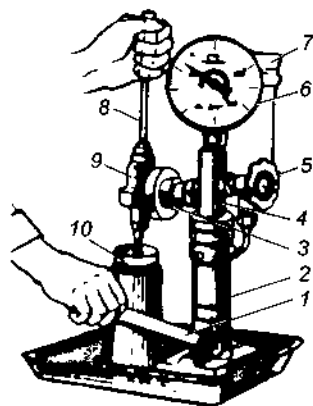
Проверка и регулировка форсунки на приборе КИ-652: 1 — рычаг; 2 — корпус; 3 — маховик; 4 — распределитель; 5 — запорный вентиль; 6 — манометр; 7 — топливный бачок; 8 — отвертка; 9 — форсунка; 10 — прозрачный защитный колпак
